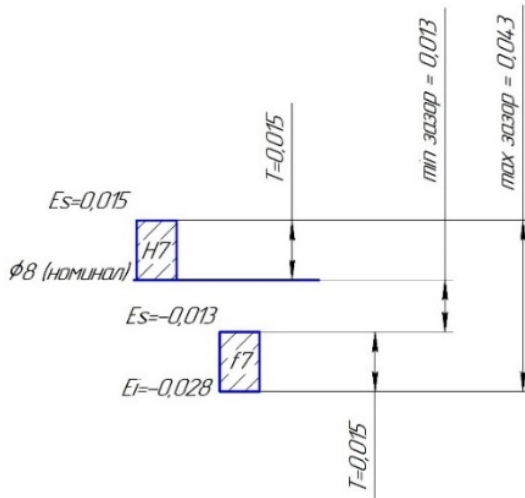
Схема полей допусков отверстия и выталкивателя
